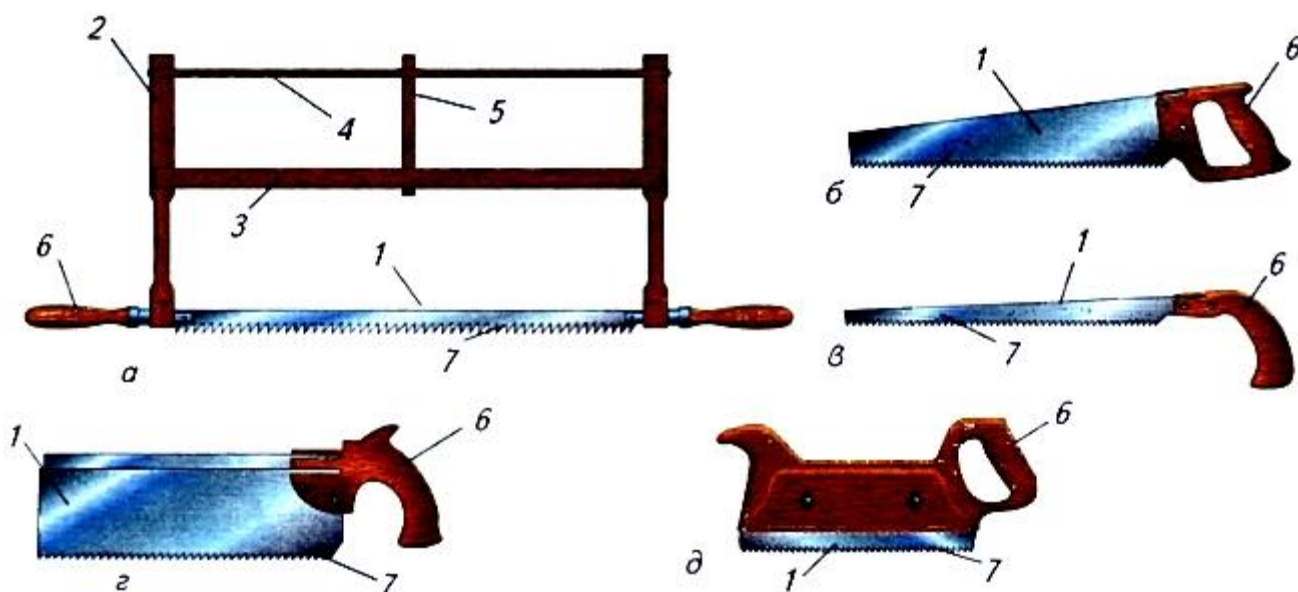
Пилы, применяемые для выпиливания шиповых соединений: а — лучковая; б — ножовка широкая; в — ножовка узкая; г — обушковая; д — наградка; 1 — полотно; 2 — стойка; 3 — поперечина; 4 — тетива; 5 — закрутка; 6 — ручка; 7 — зубья
